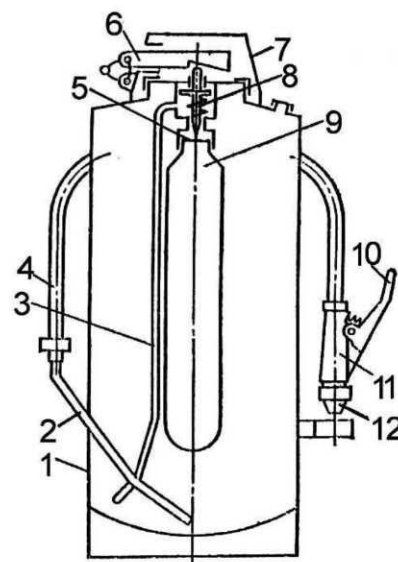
Огнетушители порошковые с газогенерирующим устройством: 1 -корпус; 2 - металлическая трубка; 3 - трубка подачи рабочего газа; 4 - прорезиненный шланг; 5 - мембрана; 6 - конусная чека; 7 - крышка головки; 8 - игла; 9 -баллончик с рабочим газом; 10 - ручка; 11 - запорный пистолет; 12 - распыляющая
